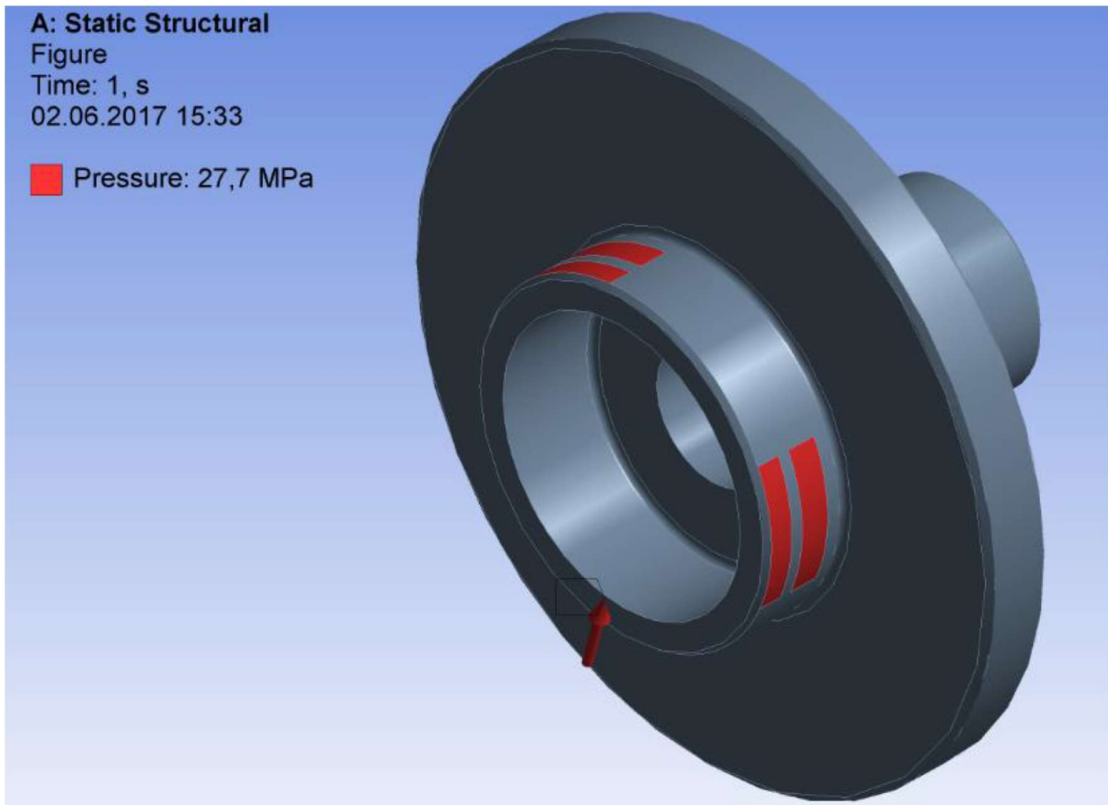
Тиск, що діє на поверхню заготовки
